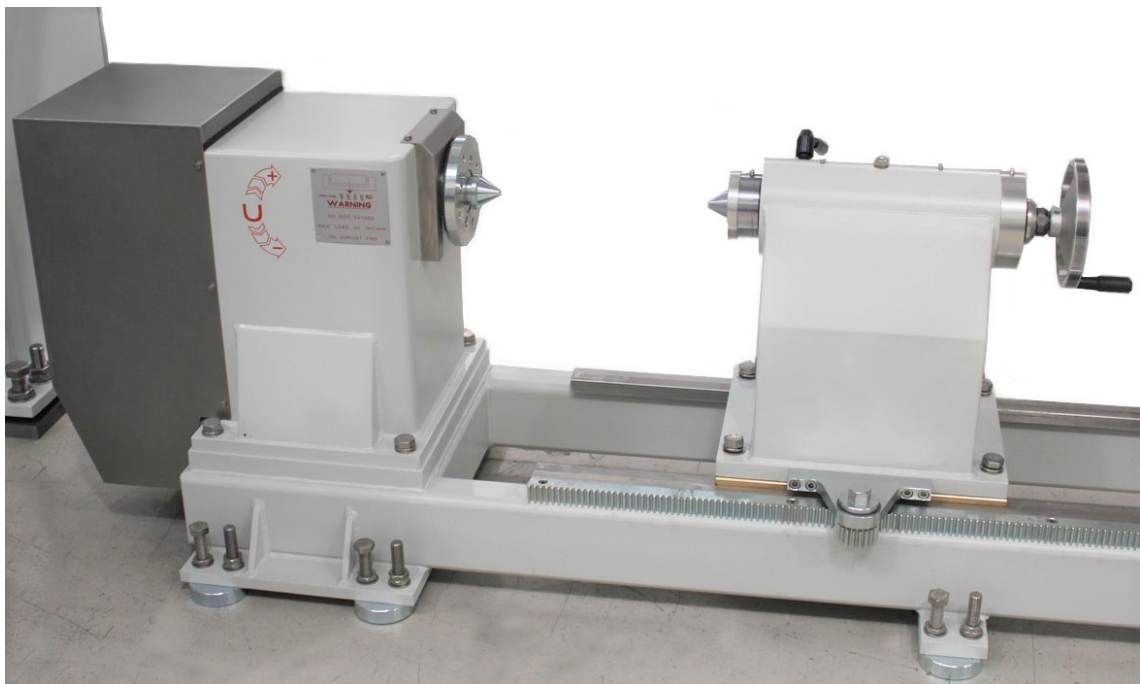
ShapeMill NCF 1600/2000 s nainstalovaným polohovacím zařízením [6]
